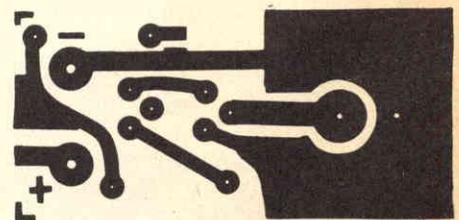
Lato rame del circuito stampato del sincronizzatore per flash di figura 12.
